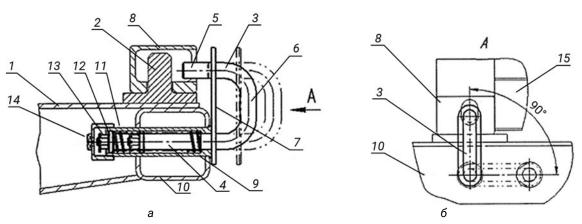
Устройство для крепления контейнера к раме вагона: 1 — рама платформы; 2 — упор; 3 — стопор; 4, 5 — концевые части скобы; 6 — средняя часть стопора; 7 — планка; 8 — отверстие фитинга; 9 — патрубок; 10 — боковая балки рамы платформы; 11 — пружина; 12 — шайба; 13 — гайка; 14 — резьбовая крышка; 15 — контейнер
